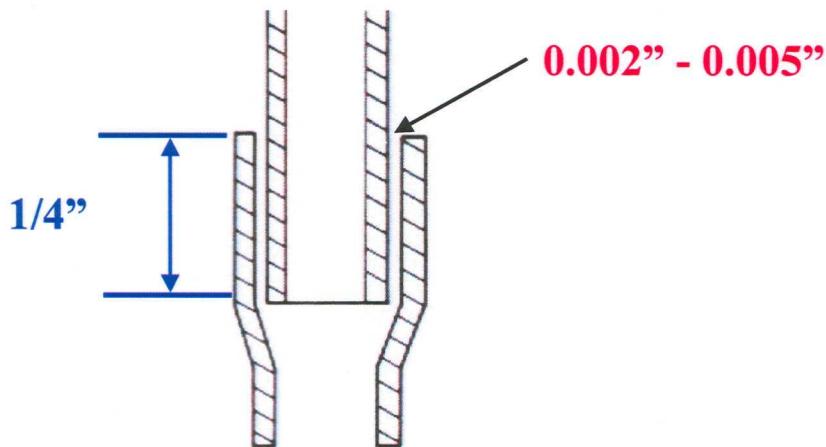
Ensamble recomendado para soldadura de tubería de cobre.
